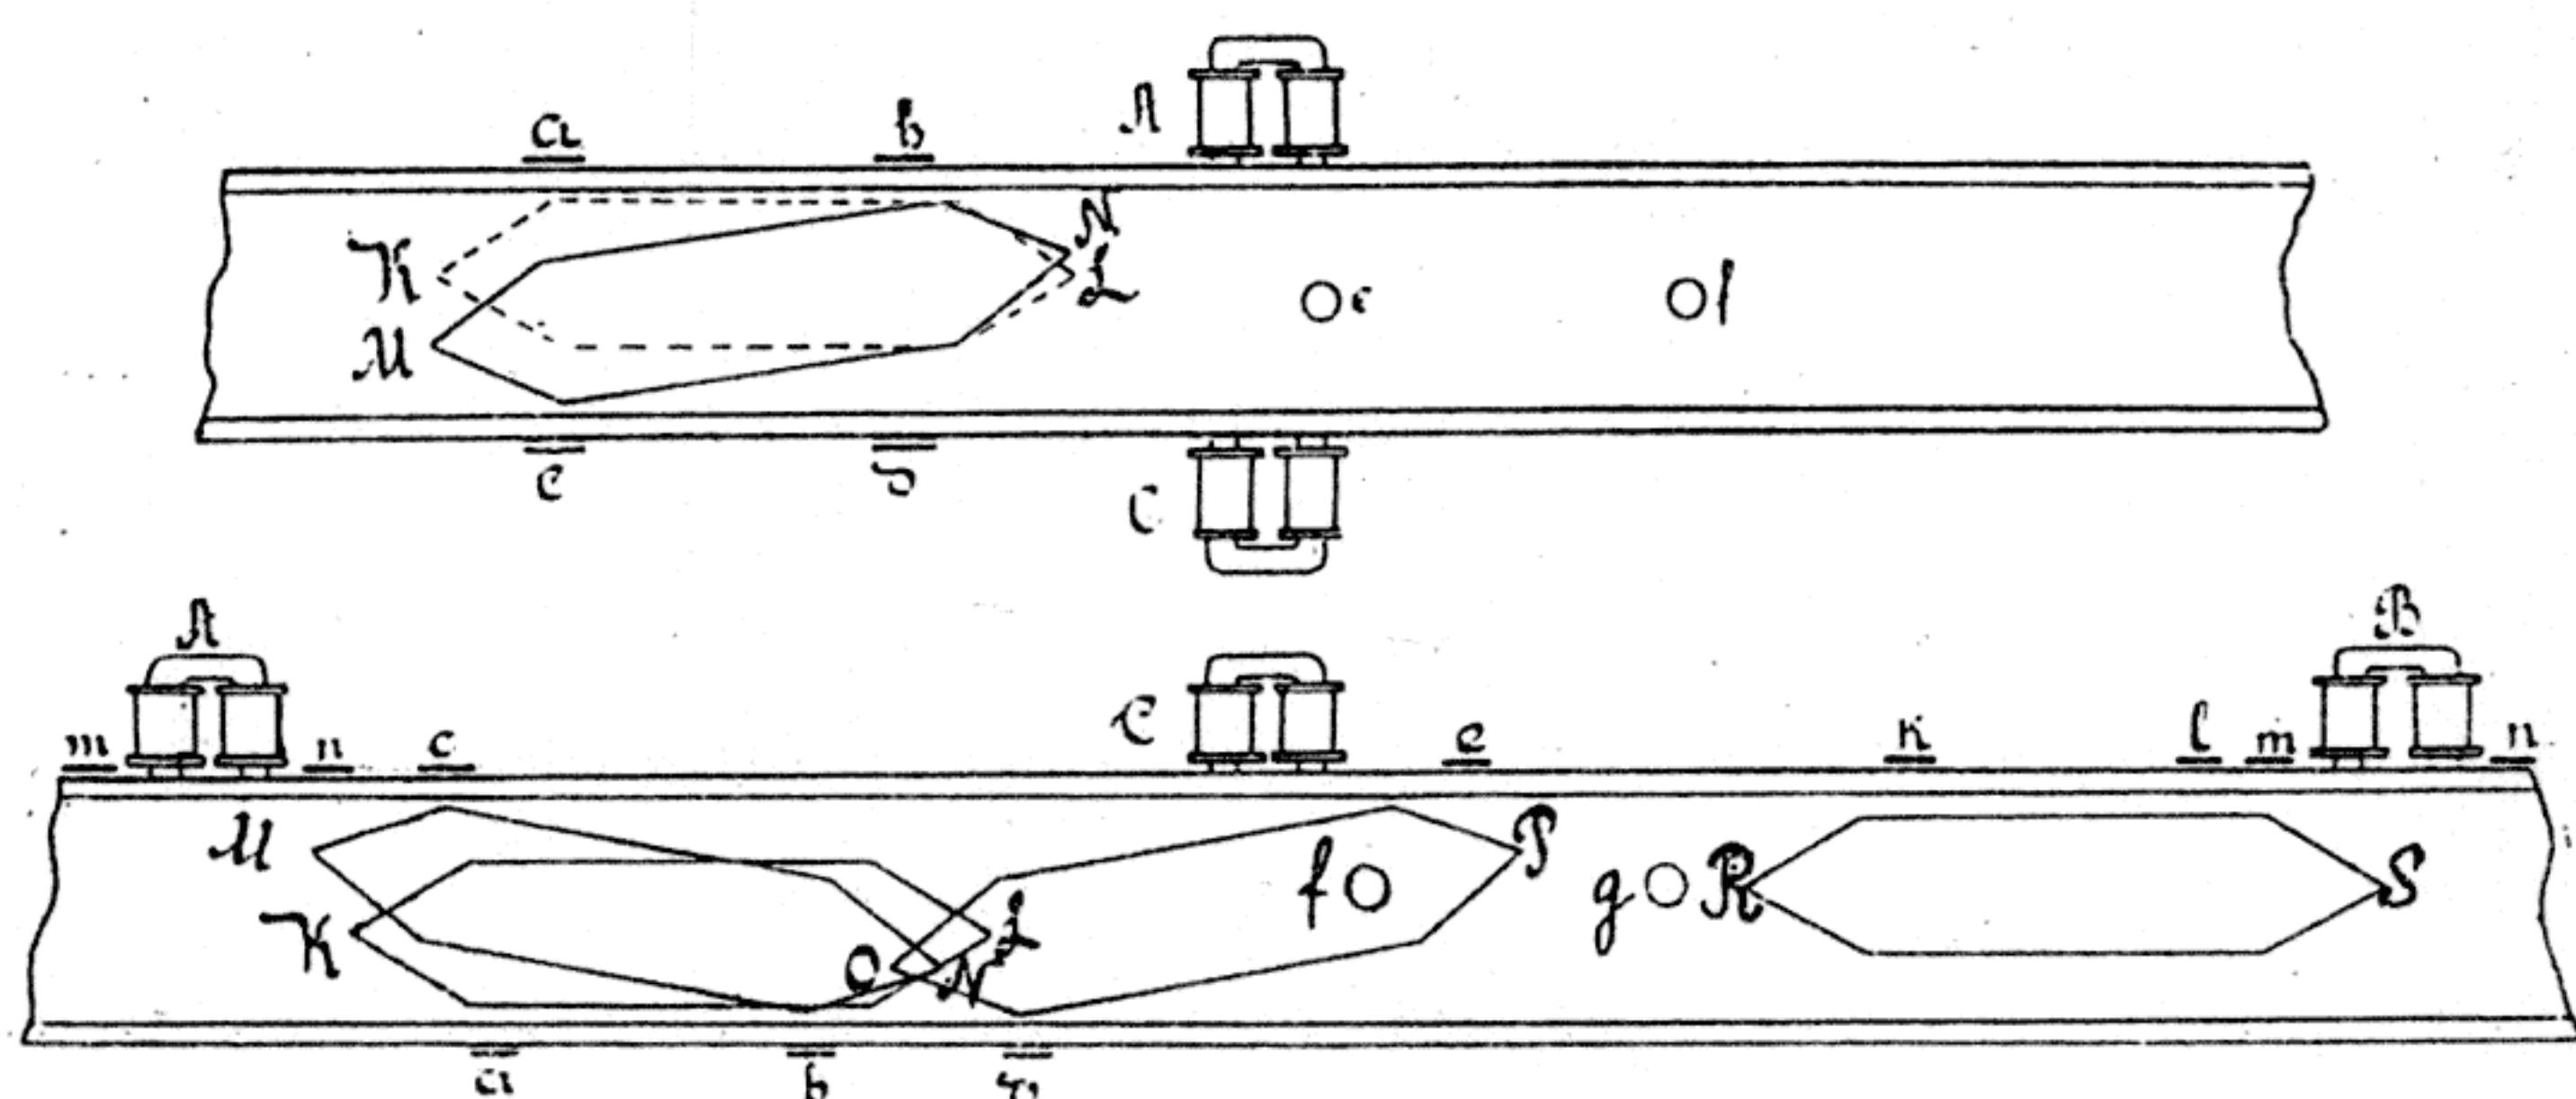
и 9. Регулирующіе боковые и верхніе электромагниты.
